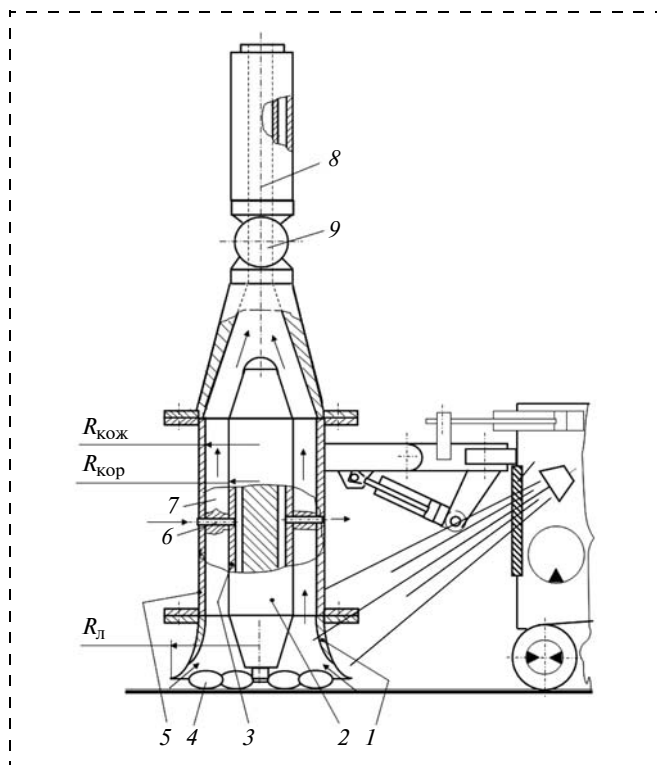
Рабочий орган грунтозаборного устройства с вертикальным расположением вала:
